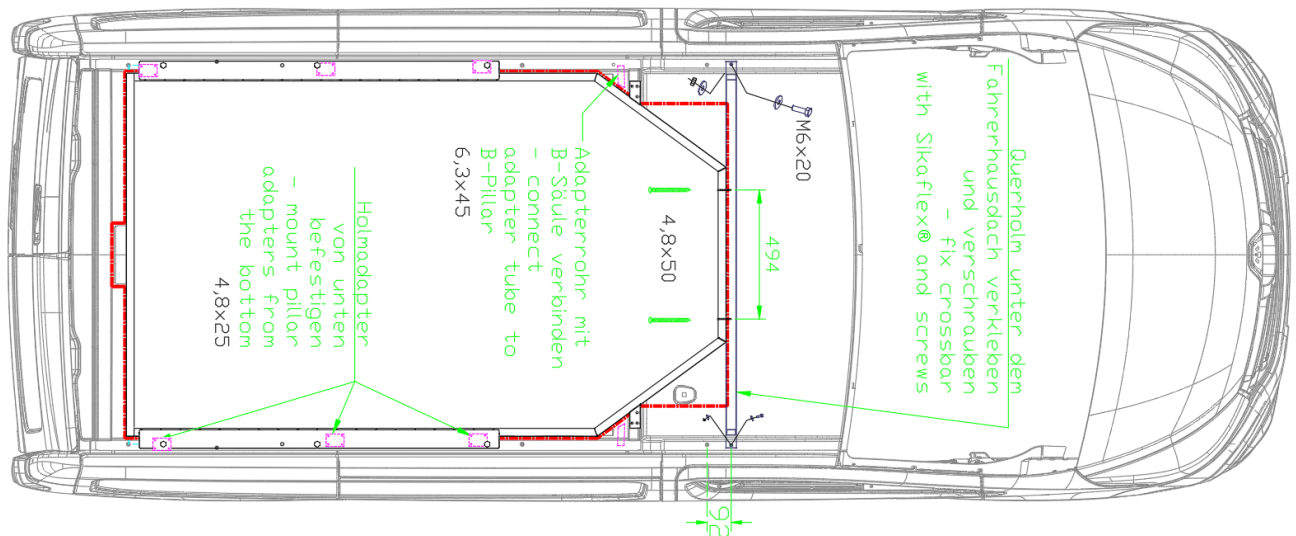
Einbaurahmen – Befestigungspunkte der Holmadapter und des Querholms / metal frame – fixing points of the pillar adapters and the crossbar [A0003929]
